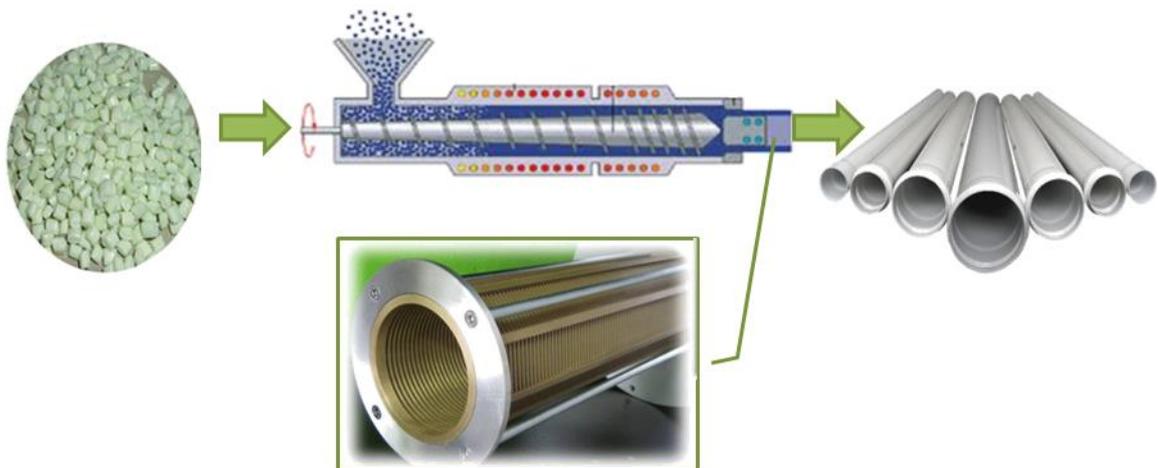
Processo de Moldagem de Tubos de Esgoto.
